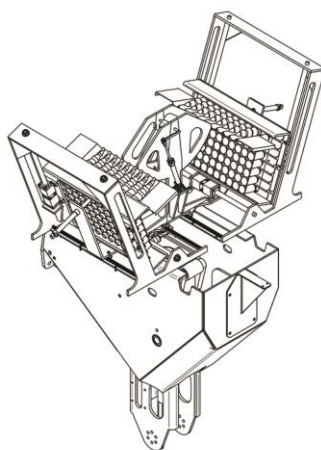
Planta faller ner mot planteringsröret på Bracke P11.a.
